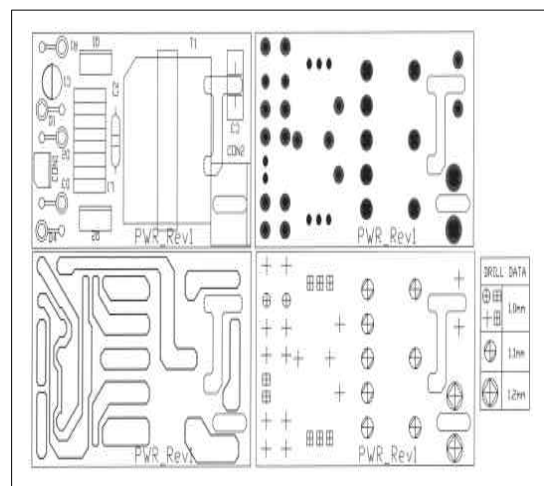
전자식 안정기 모듈 부분의 PCB 레이아웃
